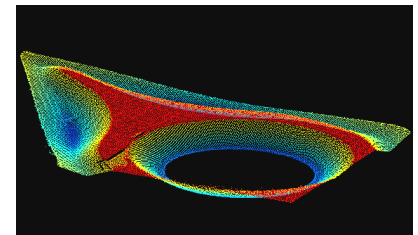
Segmentierung der Planfläche durch adaptive Ausgleichsrechnung, segmentierte Messpunkte rot markiert <sup>1)</sup>
